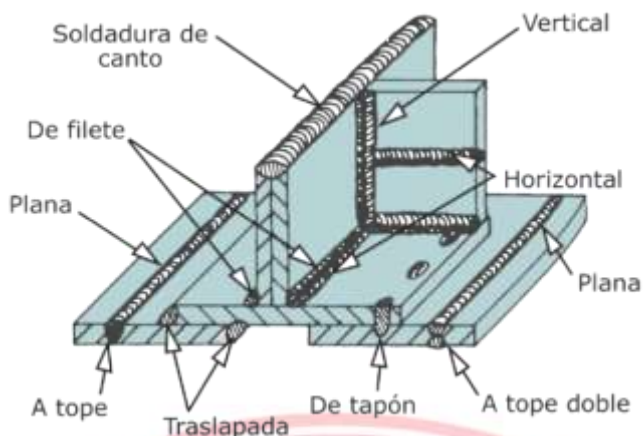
Diseños de uniones habituales en soldadura
